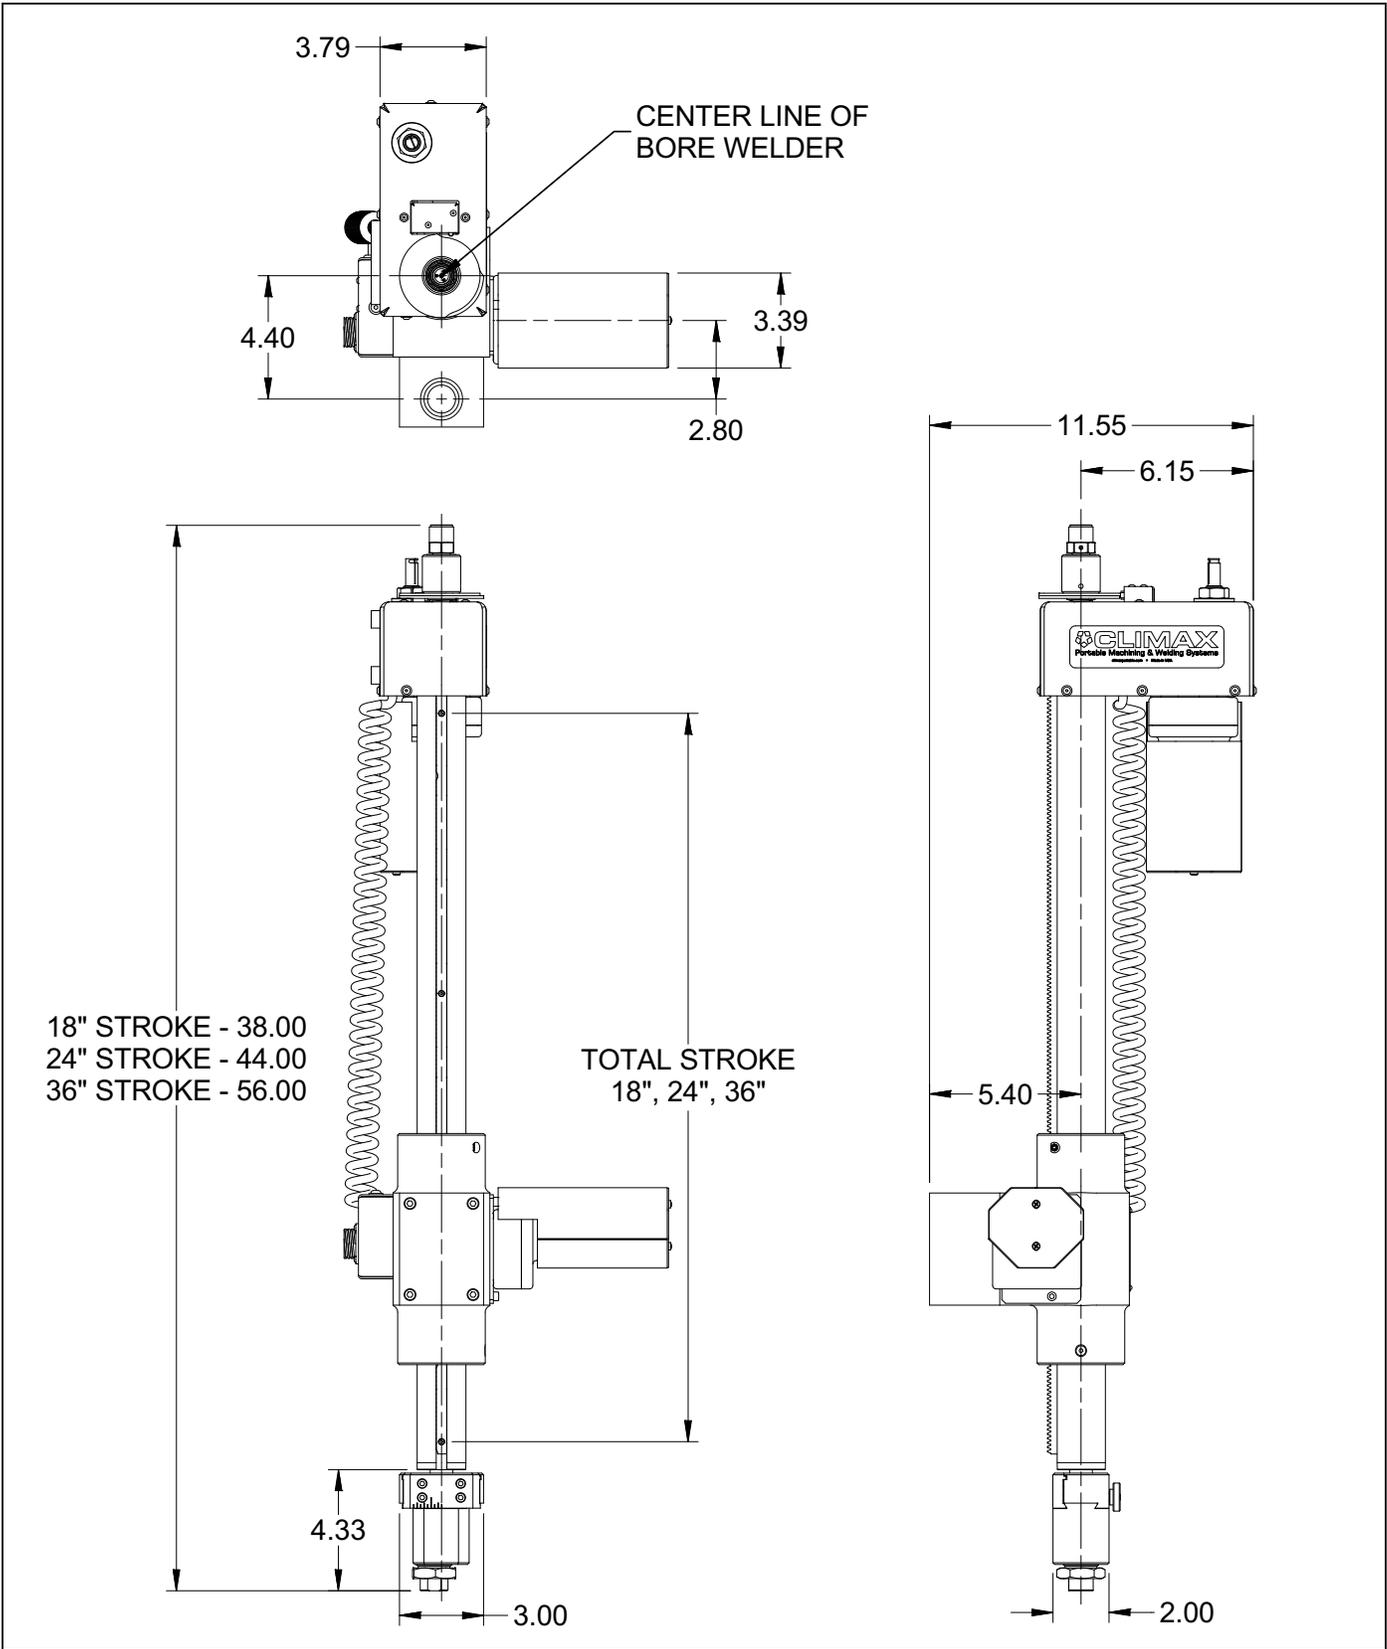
DIMENSIONS DE LA TÊTE DE SOUDAGE (RÉF. 91808)
